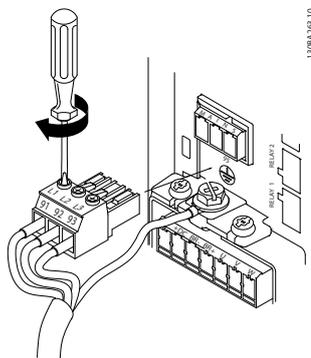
Montaje del conector de red y apriete de los cables
